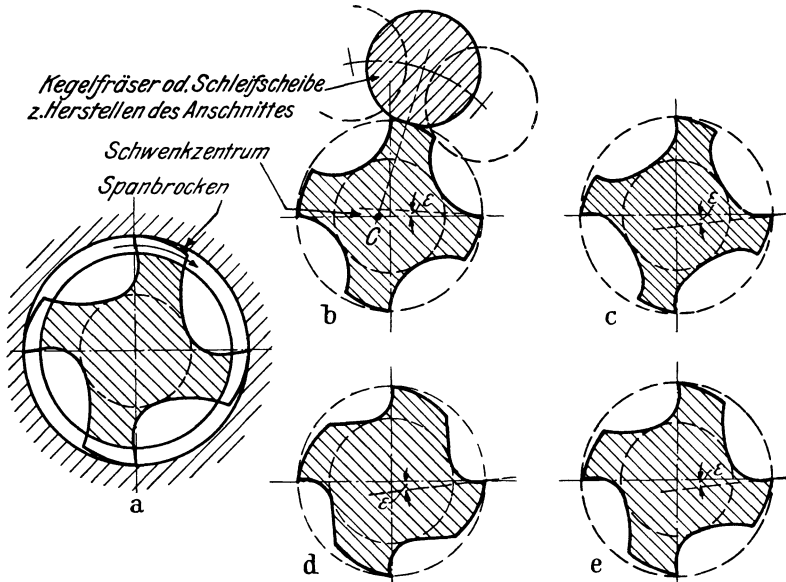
e. Hinterarbeiten der Gänge des Gewindebohrers, im besonderen am Anschnitteil.
